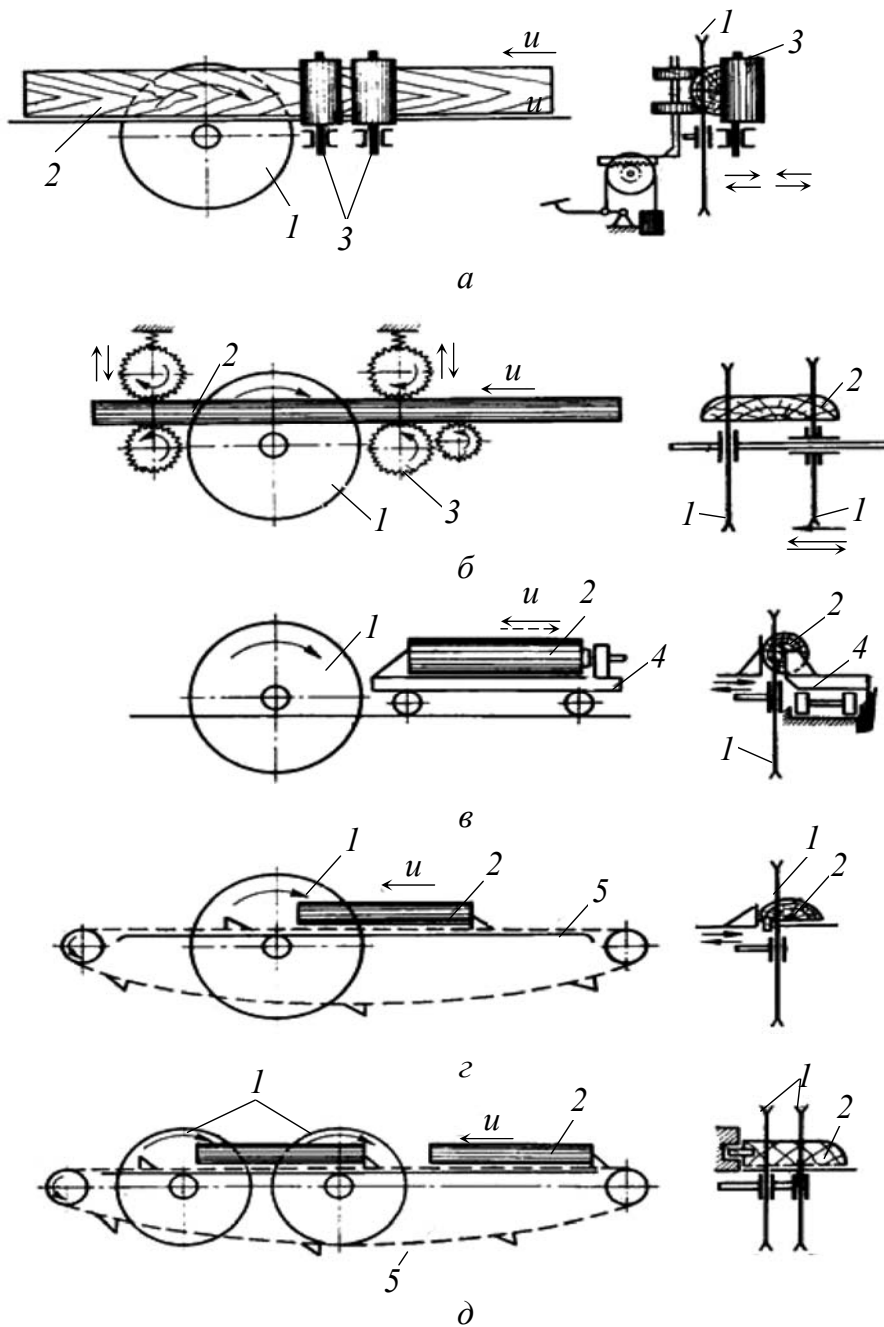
Схемы круглопильных станков для продольной распиловки:
